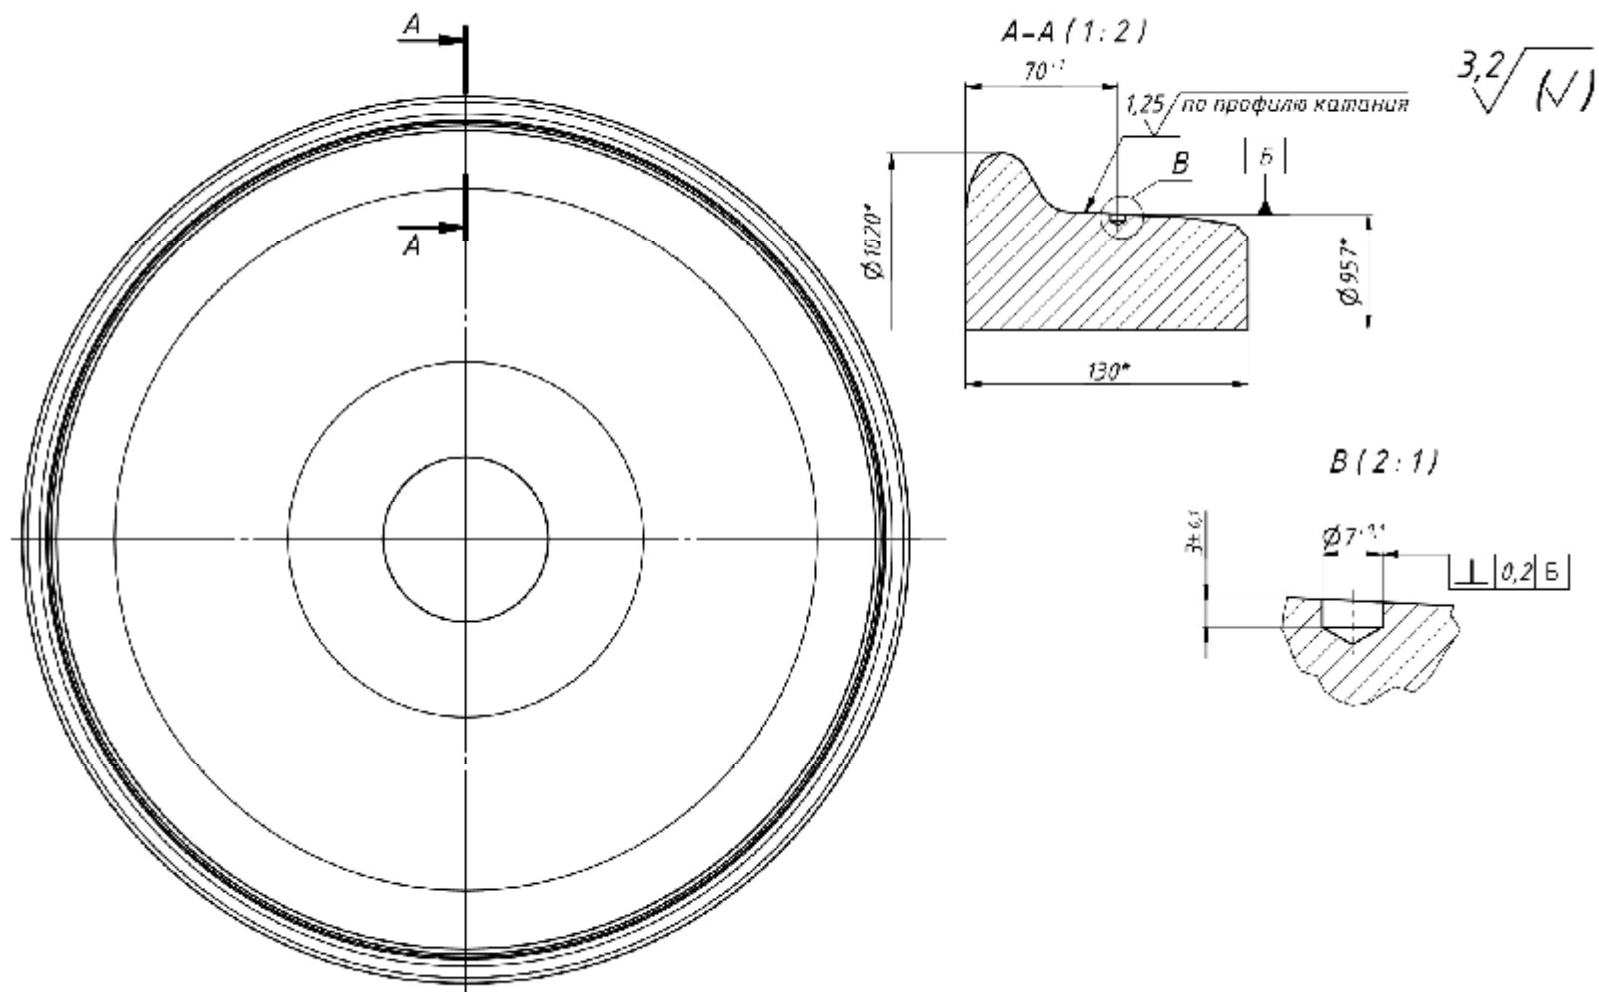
Чертеж колеса (ЭМА) меры МКП-9
